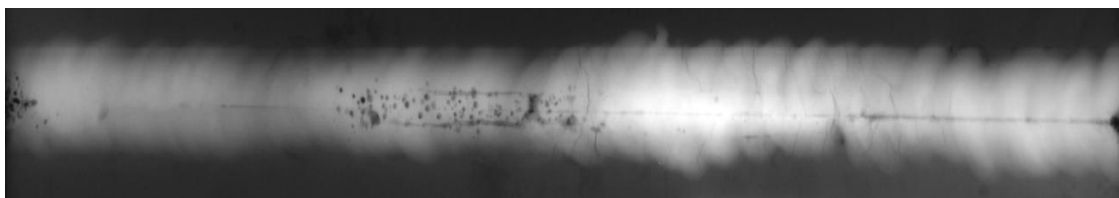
Сварной шов с примерами различных дефектов
